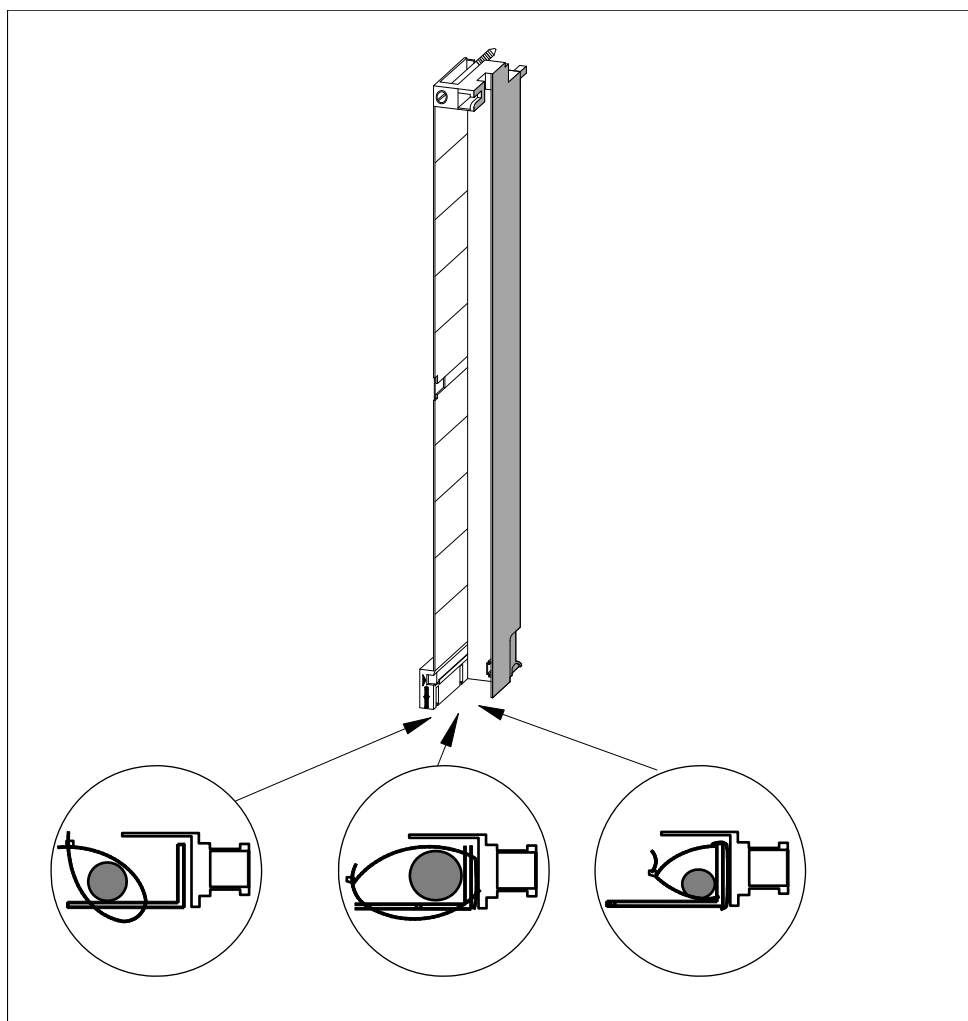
Установка компенсатора натяжения (вид снизу)
